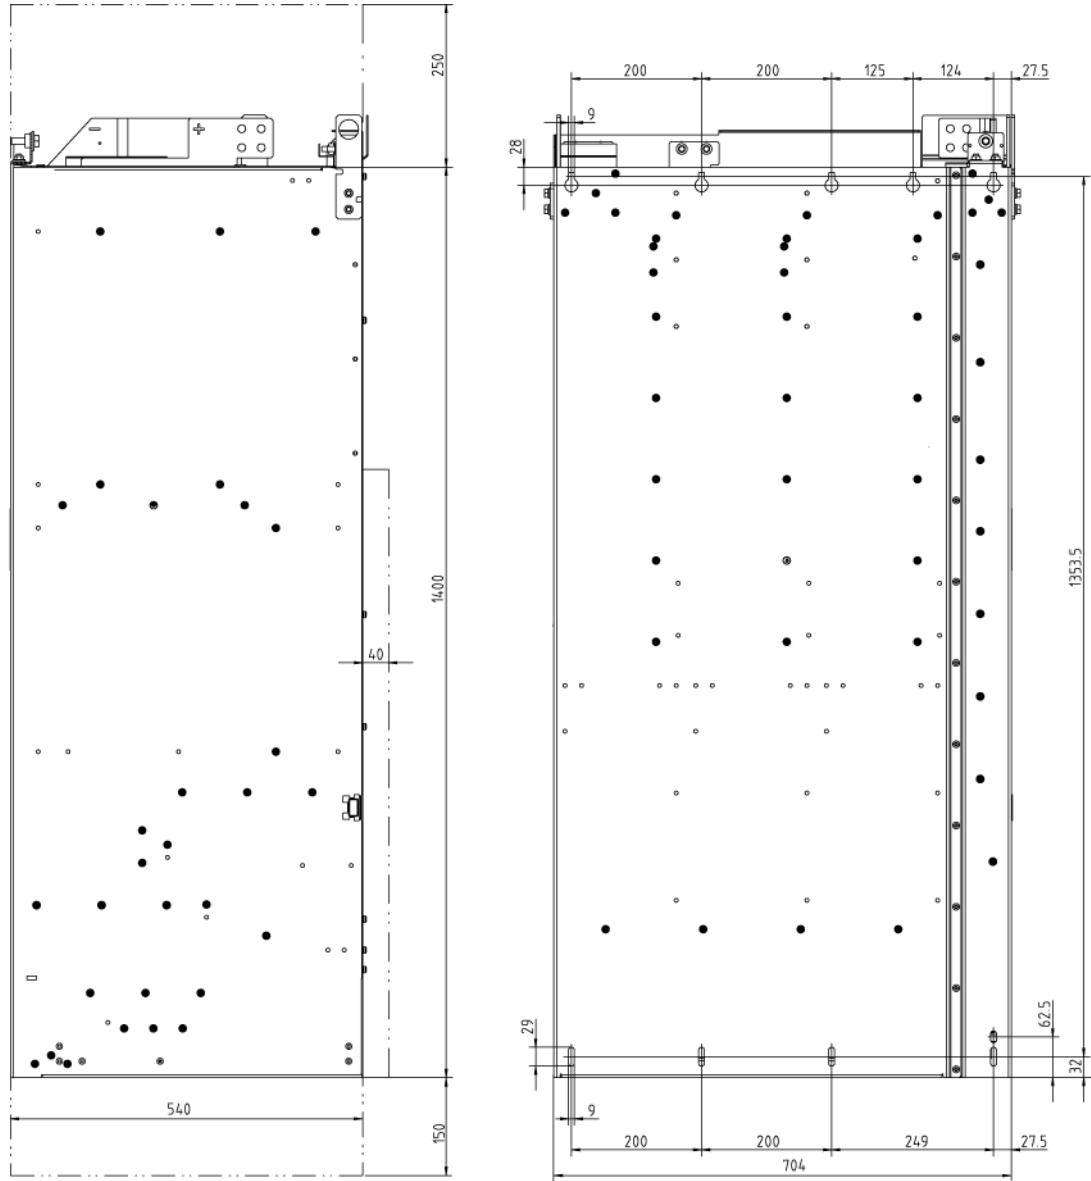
JX 型ALM的外形尺寸图侧视图和背视图
